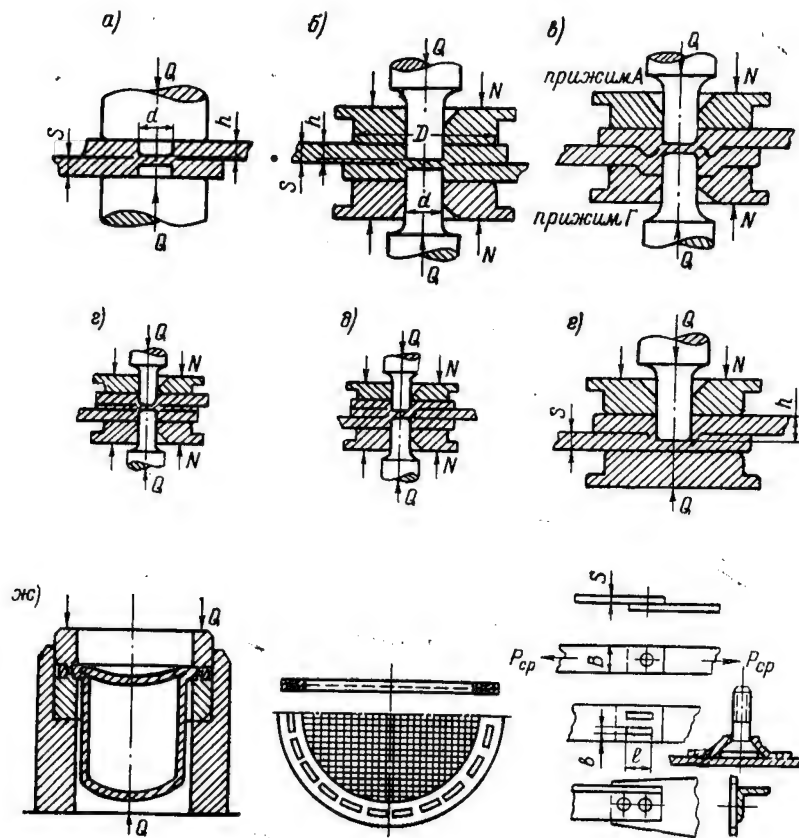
Схемы различных способов точечной и контурной сварки давлением и примеры соединений
